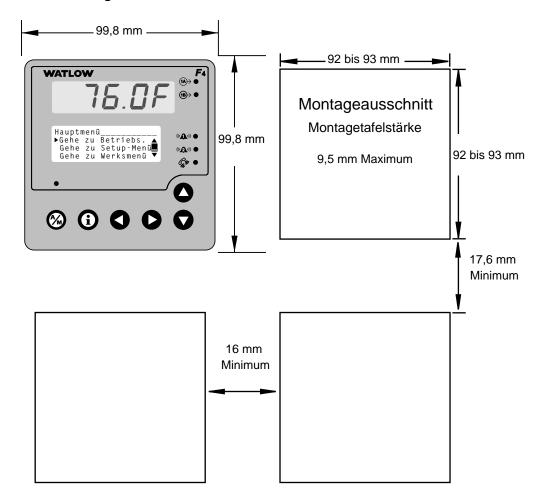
Montageausschnitt – Abmessungen der Serie F4P.
